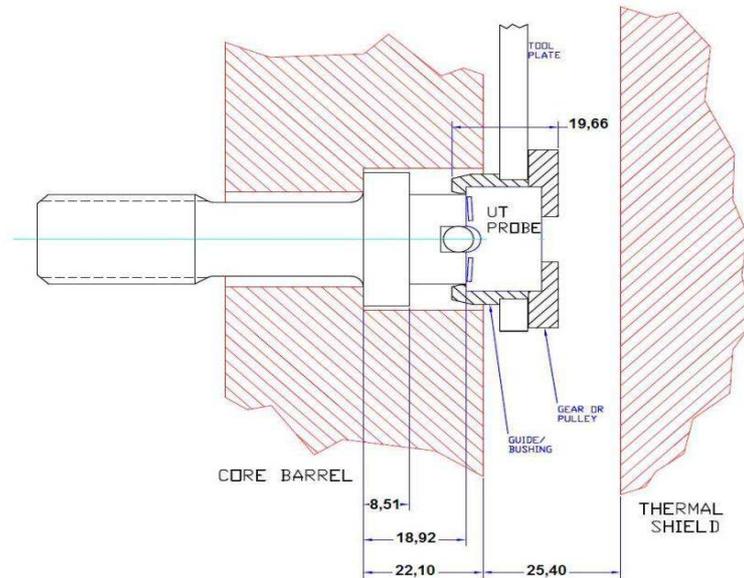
Zeichnung: Prüfsituation für die Ultraschallprüfung von Kernbehälterschrauben hinter dem Thermoschild
